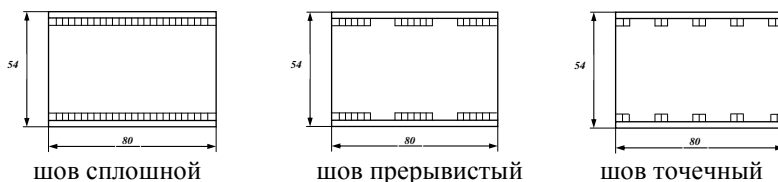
Вид А: соединение стальных элементов сварными швами
